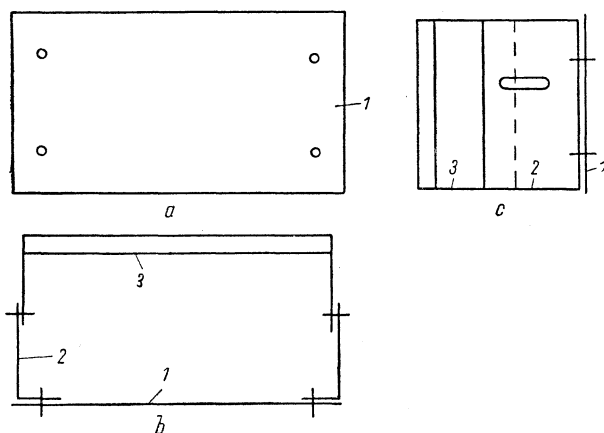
Frontplatte und Chassis für die Flachbauweise; Frontplatte (1), Blechwinkel (2), Chassis (3), Vorderansicht (a), Draufsicht (b) und Seitenansicht (c)
